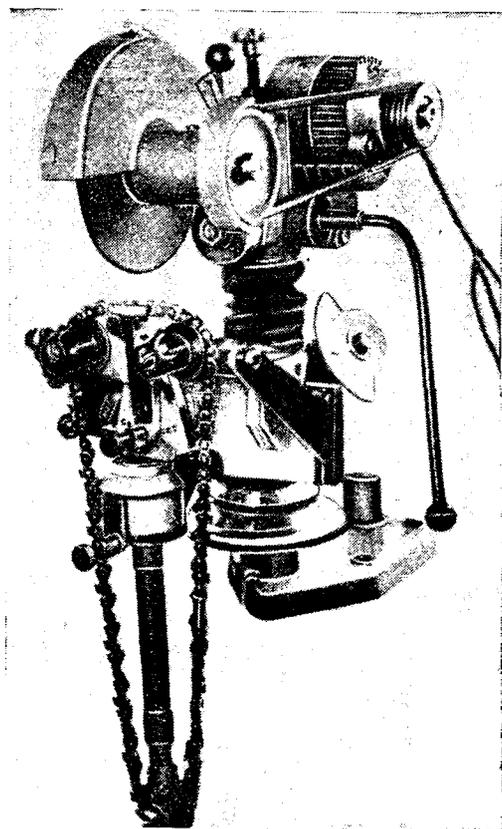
Заточный станок ЦНИИМЭ УЗС-5
